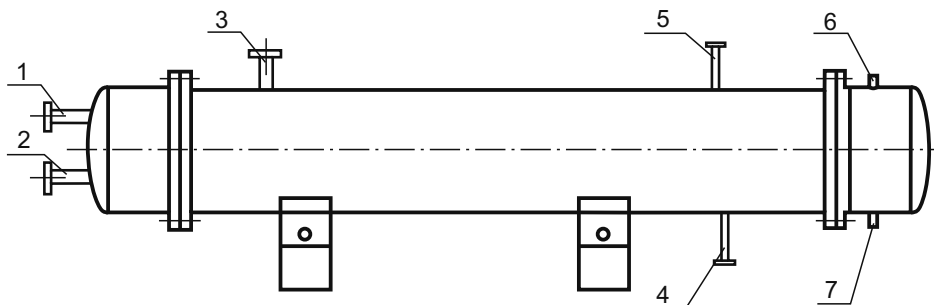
Габаритные и присоединительные размеры подогревателя мазута
